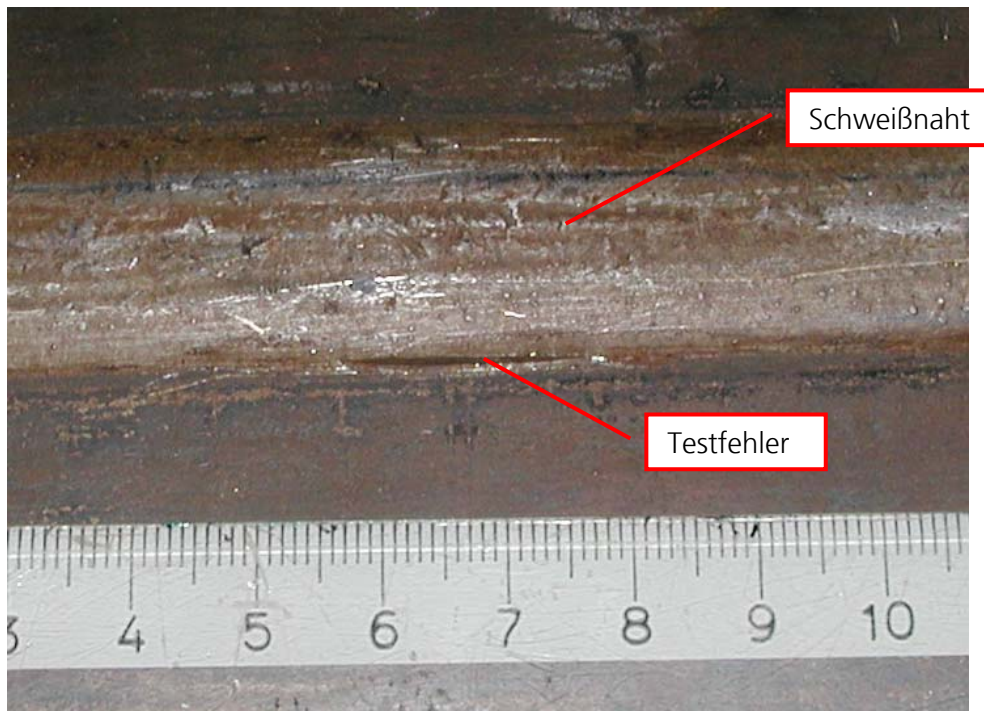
Rohrsegment mit Testfehler (Sägeschnitt, 16 x 1,5 mm²) an der Längsschweißnaht
